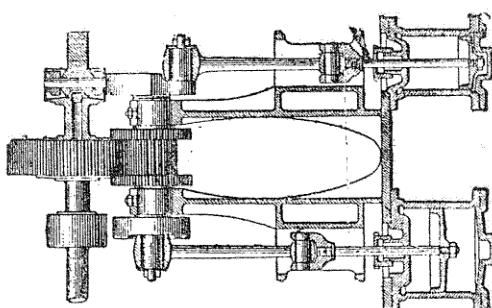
Moteur de Dion et Bouton. Coupe en plan
